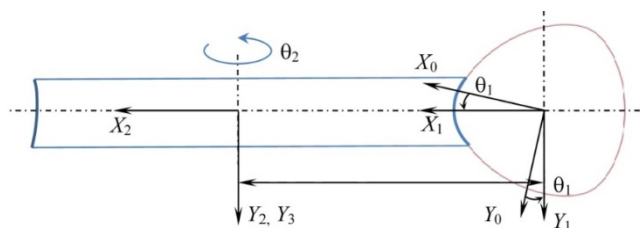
Схема фрезопротягивания РК-профильного вала с поперечным расположением оси инструмента
